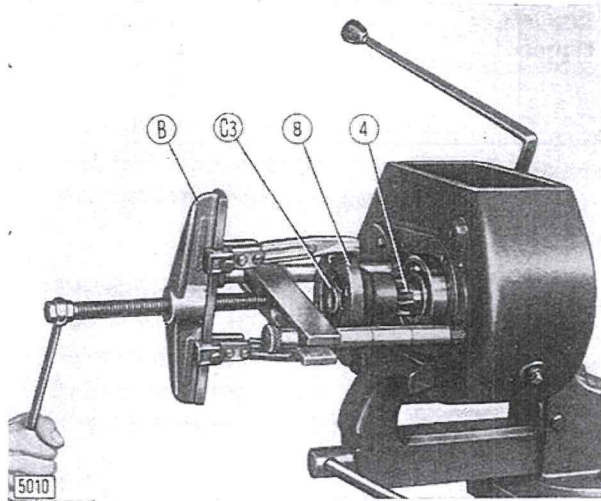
Smontaggio dell'albero inferiore completo di cuscinetti mediante l'estrattore universale A 537105 (B).
